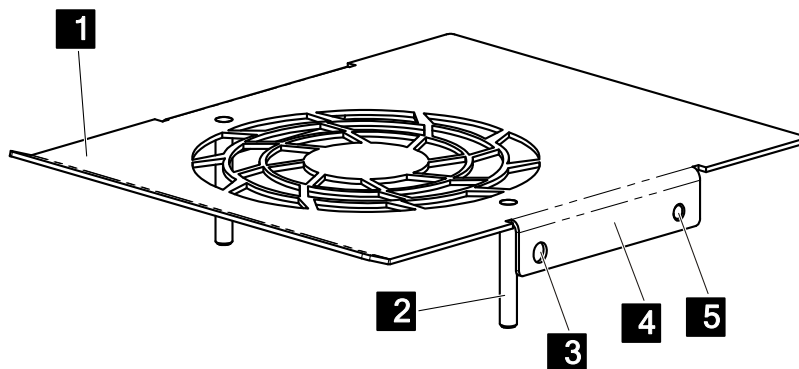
Крышка F20 с направляющими штифтами для насадки вентилятора
